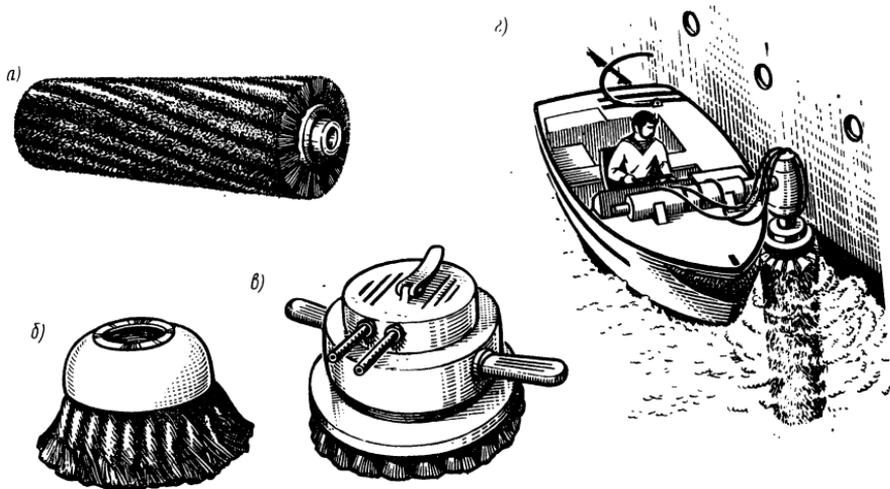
Щеточный инструмент для очистки от обрастаний: а — цилиндрическая щетка; б — торцовая щетка; в — ручная пневматическая щеточно-зачистная машинка; г — надводная установка для подводной очистки поверхностей.
